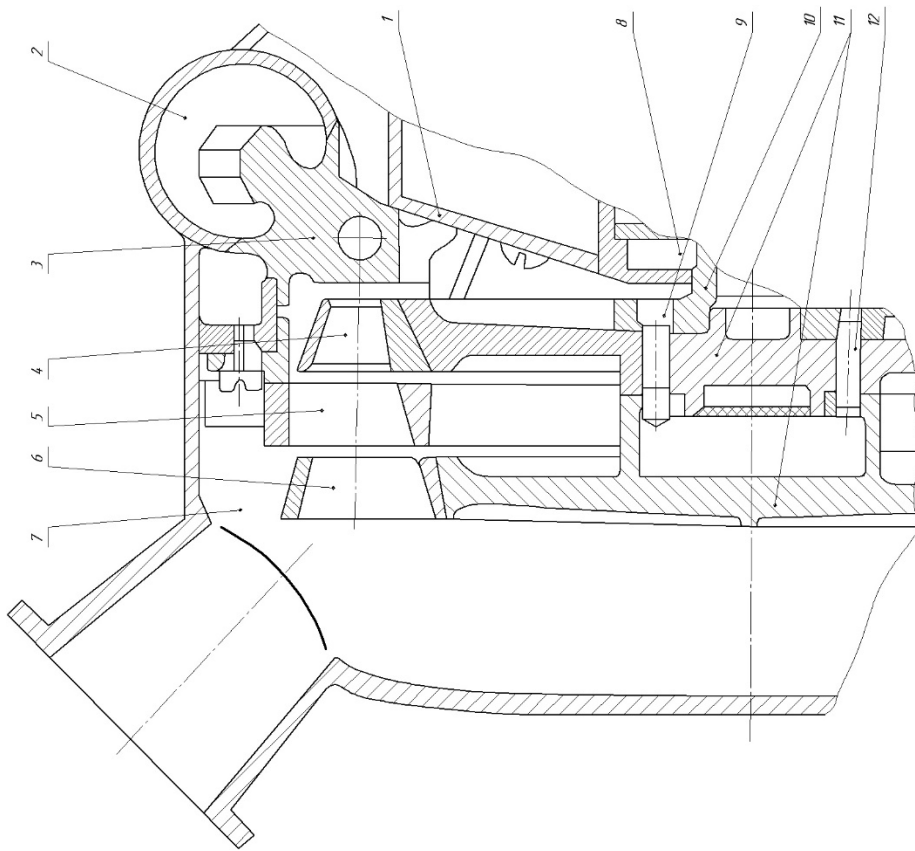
Конструкция двухступенчатой осевой активной турбины
